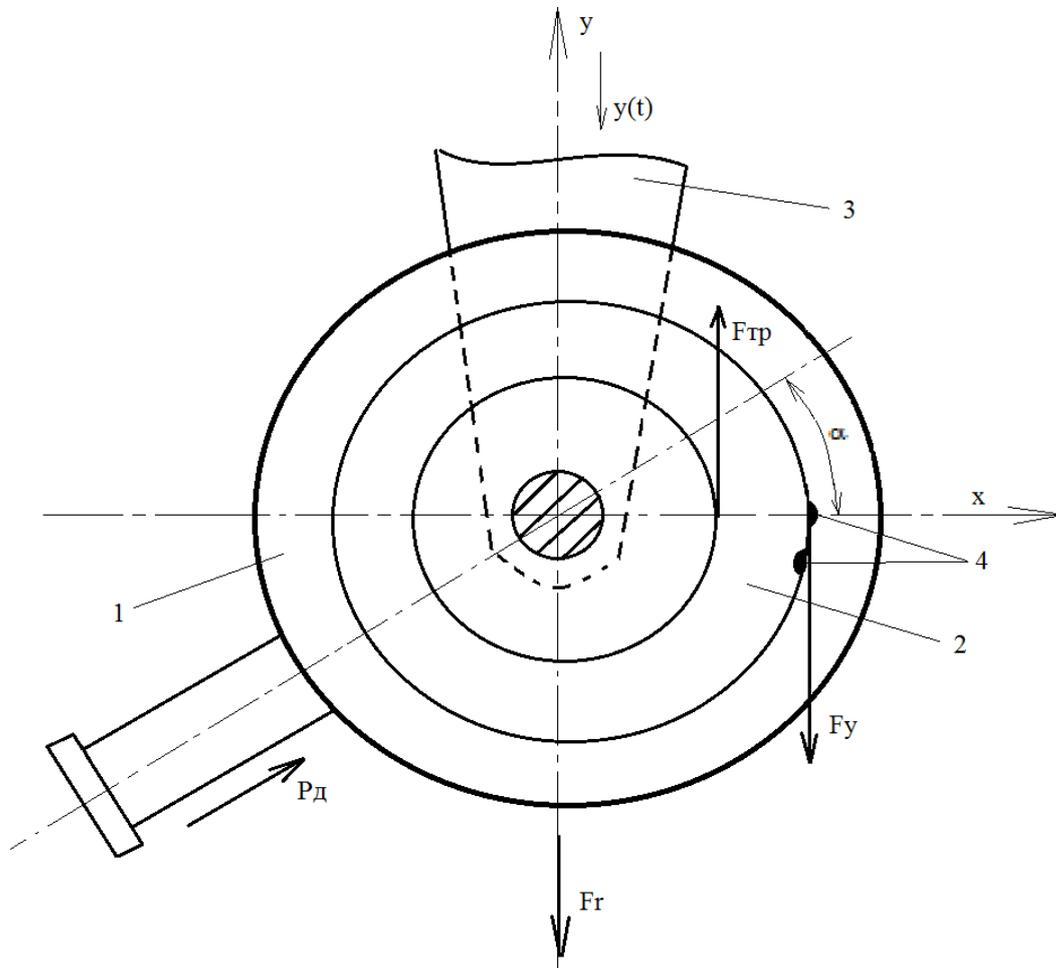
Схема процесса проворачивания вкладыша сферического подшипника в корпусе наконечника демфера несущего винта
